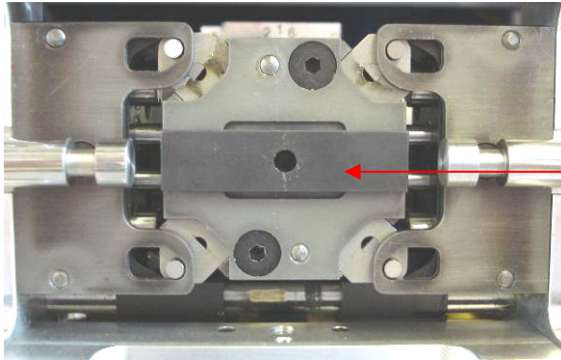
Hülsenhalteeinheit / Ferrule holding unit
